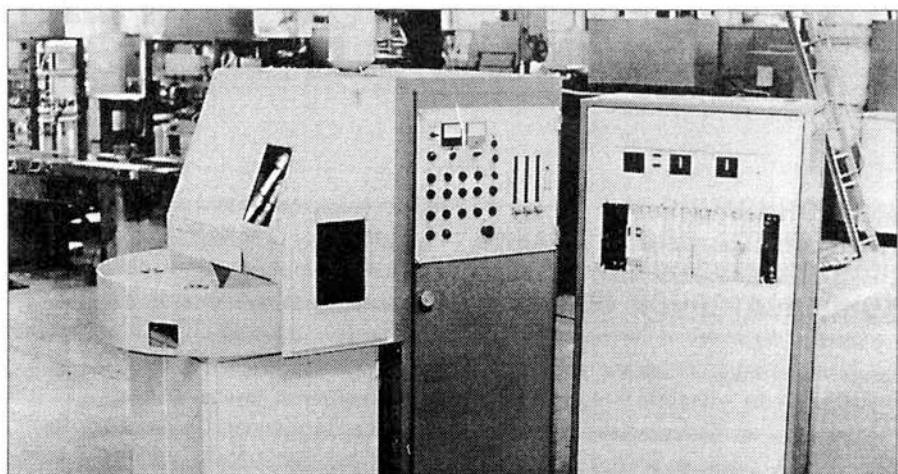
Внешний вид специализированной установки УП-142 для плазменно-порошковой наплавки
